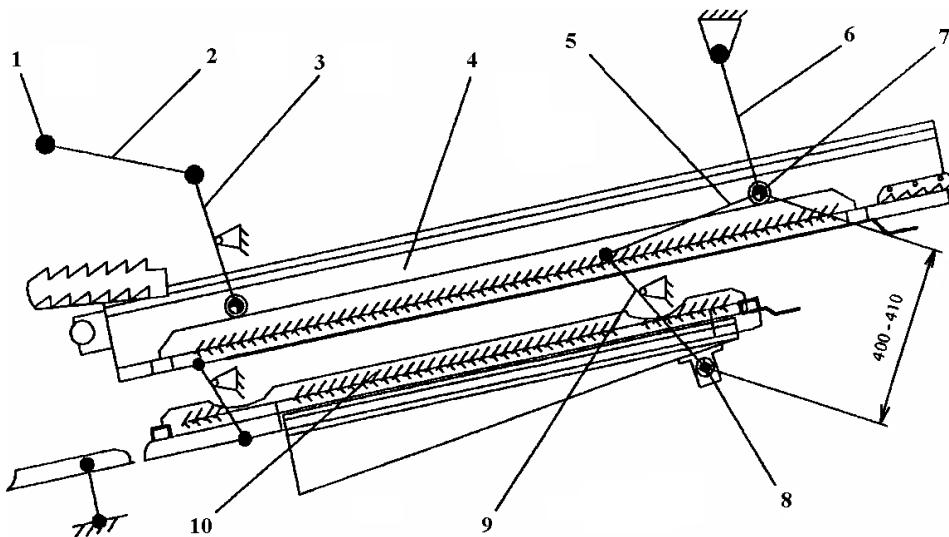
Механізм коливання решіт: 1 – опорні підшипники коливального вала; 2 – шатун; 3 – приводний важіль; 4 – верхнє решето; 5, 6 – підвіска; 7 – задня вісь кочення верхнього решета; 8 – нерухома вісь кочення важелів решіт; 9 – двоплечий важіль; 10 – нижнє решето
